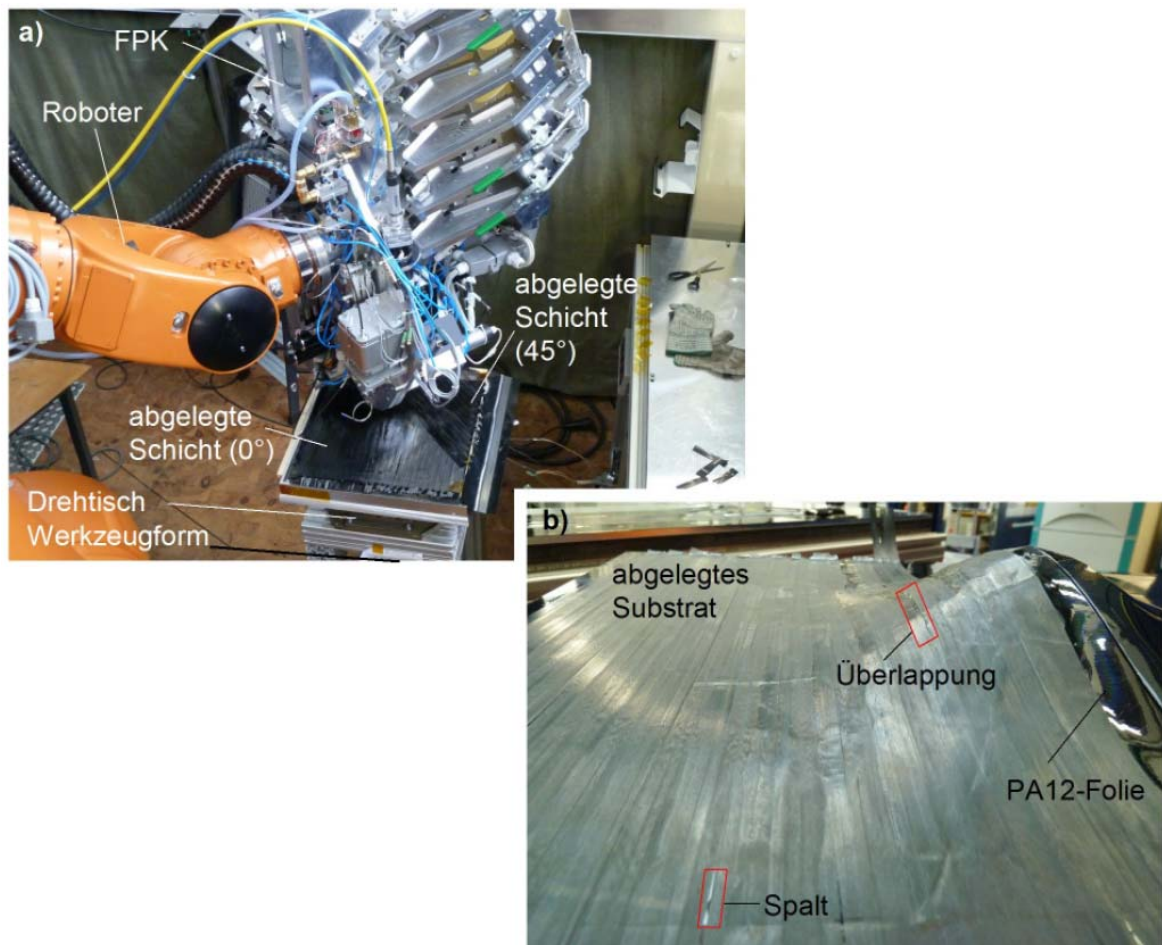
Versuchsaufbau für erste Ablegeversuche auf einer 3D-Werkzeugform
